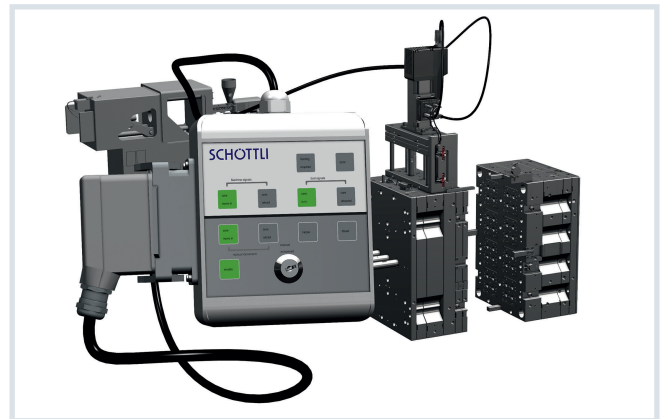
Das E-Drive-System ist für Probwerkzeuge und Ausdrehwerkzeuge bis 64 Kavitäten geeignet © Schöttli/Husky
